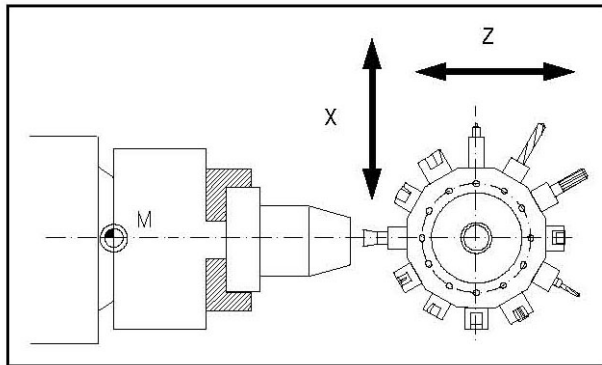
Steuerbare NC-Achsen an einer Drehmaschine
